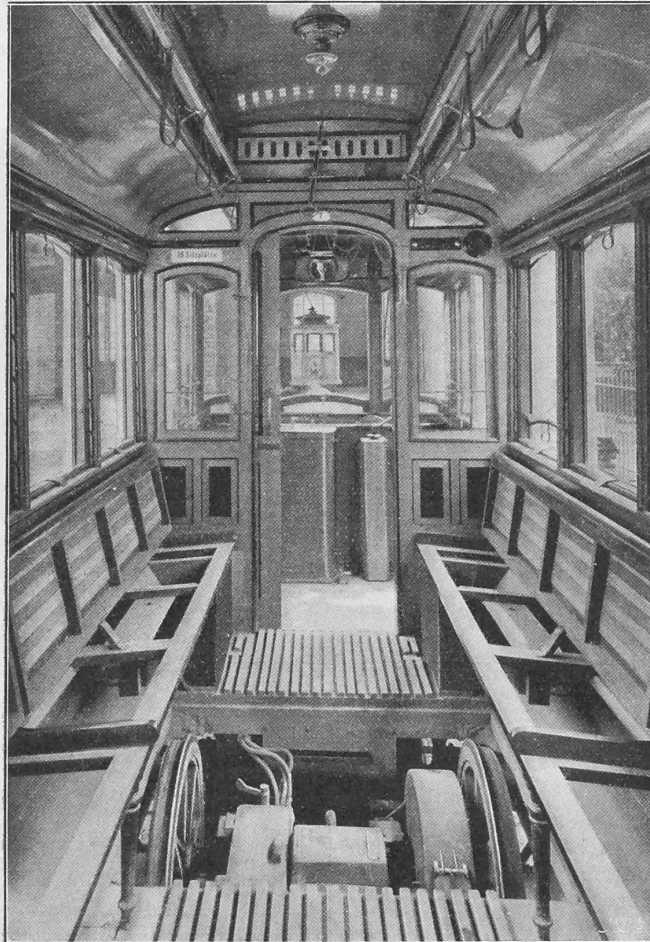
Innenansicht des Wagens mit abgehobenem Fussboden.
